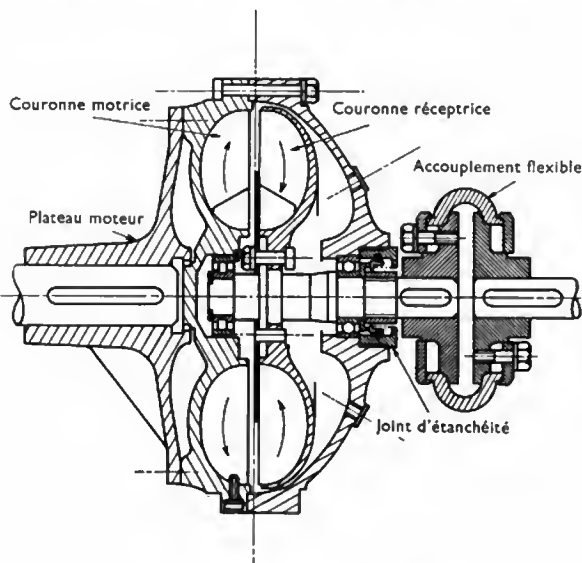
Coupleur hydraulique (Ferlec-Sinclair)
